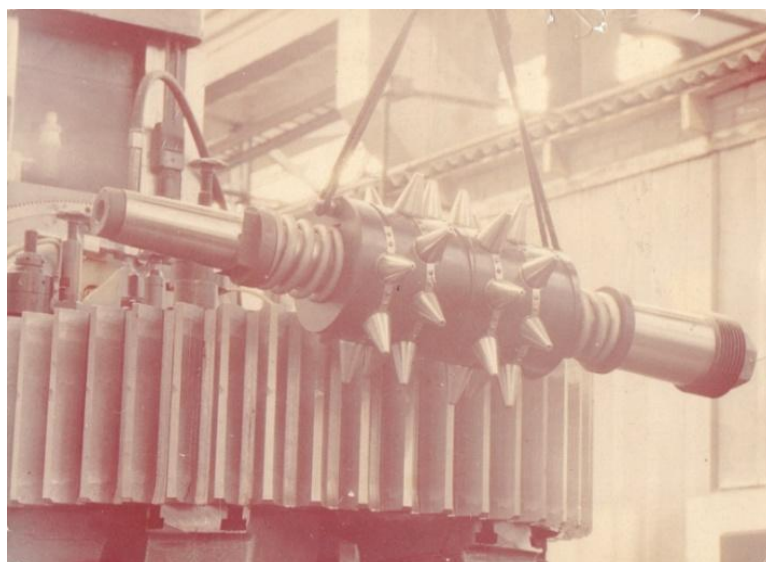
Встановлення черв'ячного накатника, $m = 20$ мм, з конічними накатними роликками для накатки зубців циліндричного зубчастого колеса.
